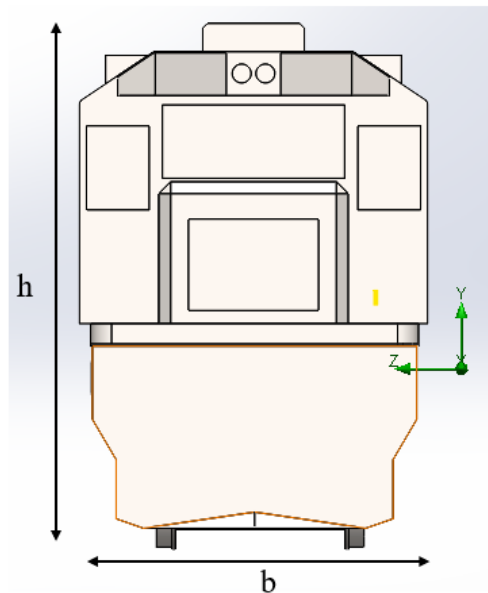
Parte frontal de la locomotor GT42AC. Fuente propia
